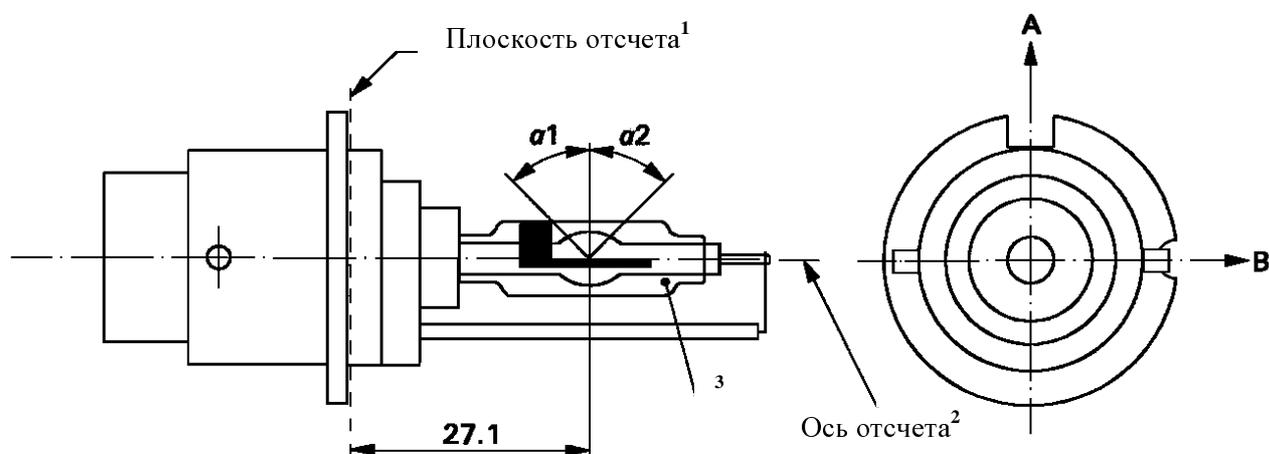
Категория D4R - Типовой газоразрядный источник света с соединительным устройством -
